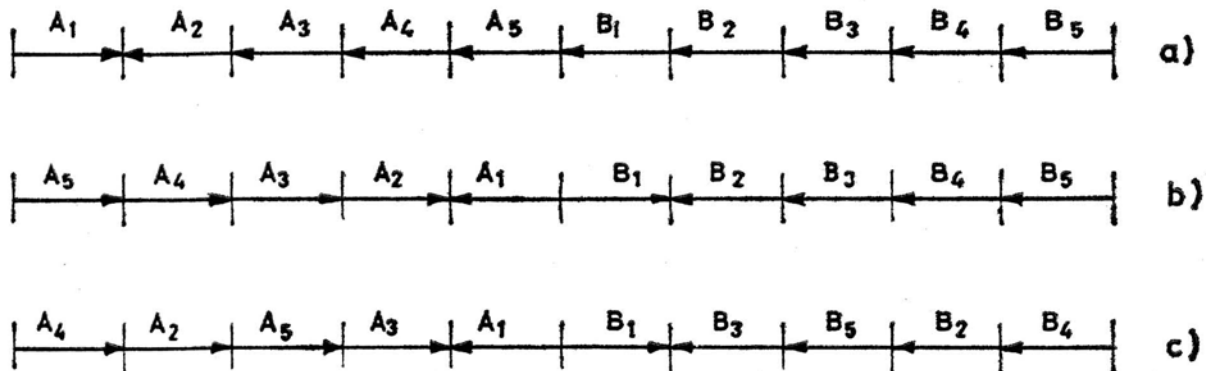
SOLDADURAS A PASO DE PEREGRINO CON DOS SOLDADORES
